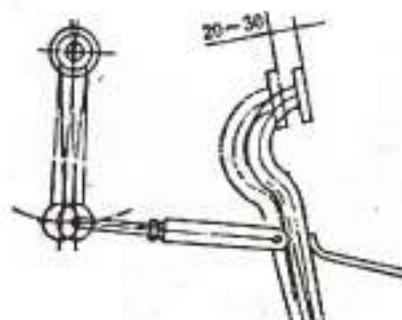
Регулировка свободного хода педали муфты сцепления
